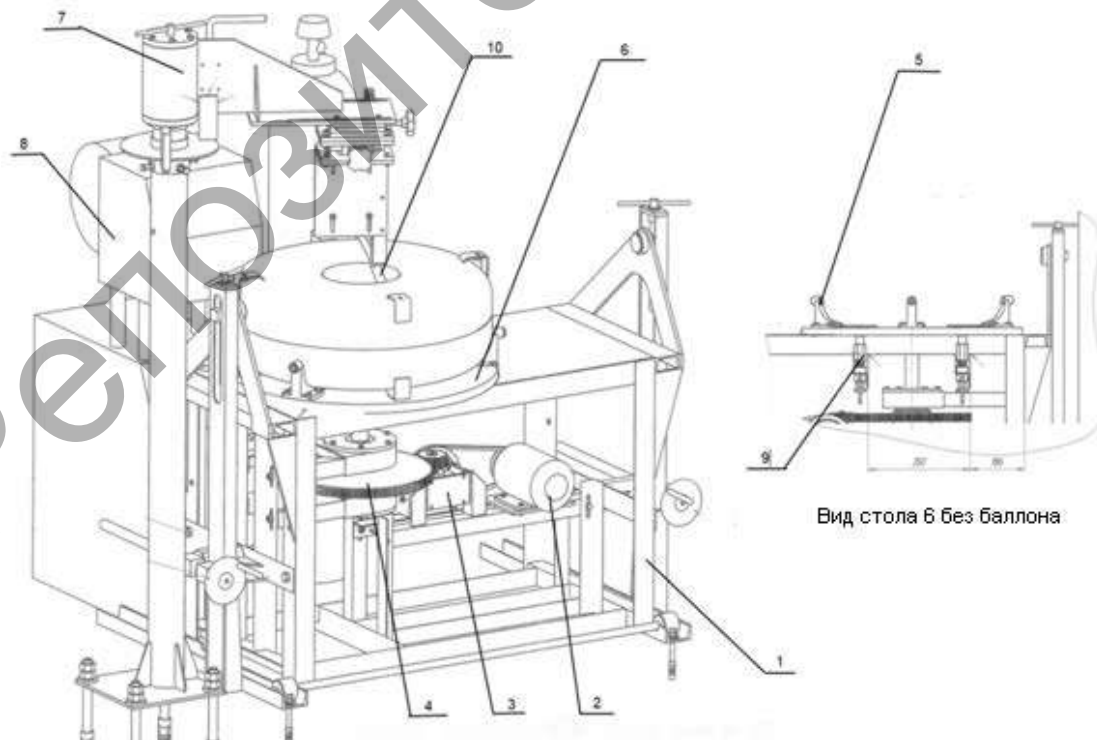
Общий вид стенда для сварки центрального днища
